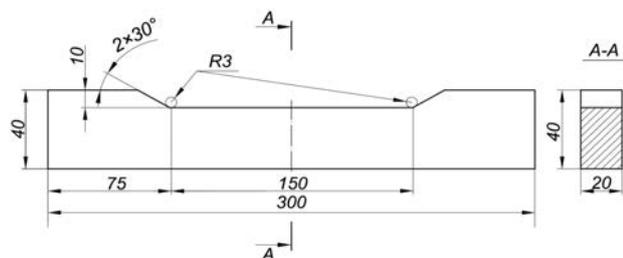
Эскиз заготовки образца для исследования усталостной долговечности с разделкой под наплавку размерами 10x20x150 мм
